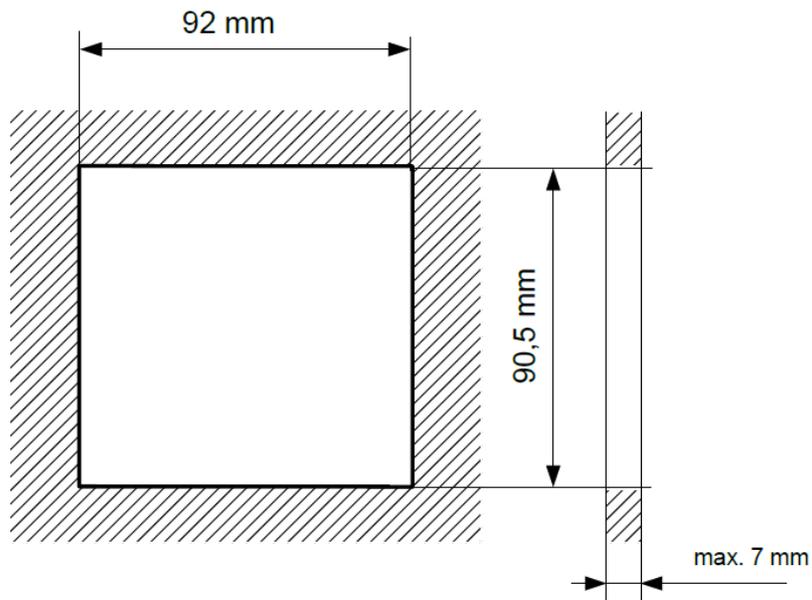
Zulässige Abmessungen der Montageöffnung
